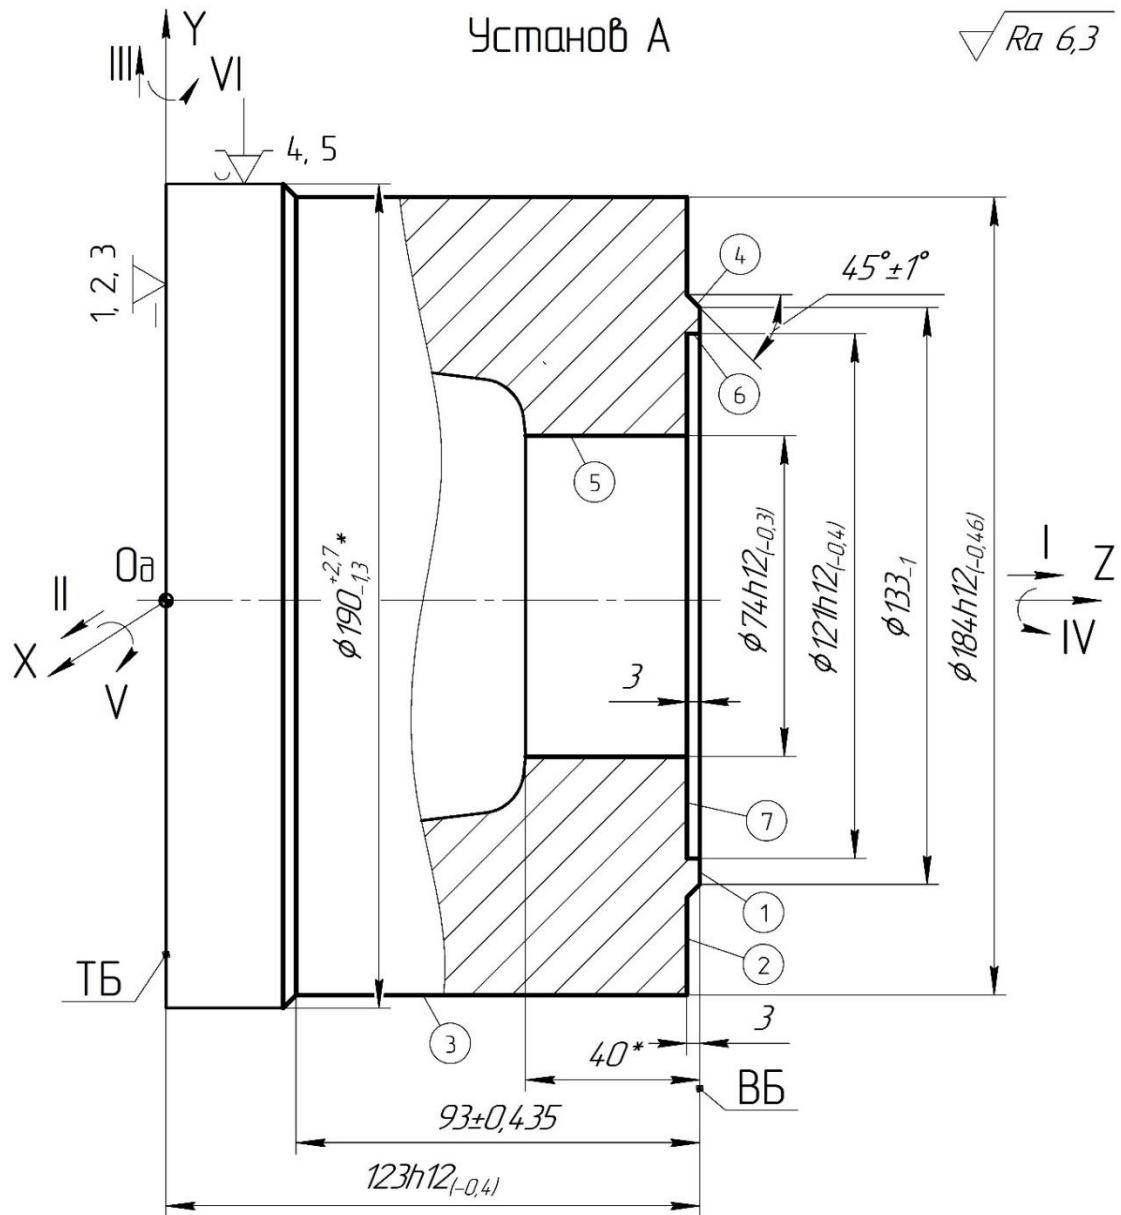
Схема установки заготовки на операції 015 «Токарна з ЧПК».
